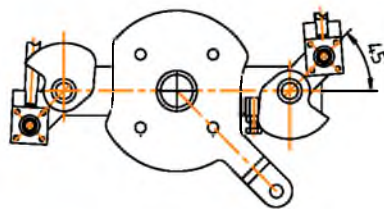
Разъединитель трехполюсный (ведущий полюс в центре)
